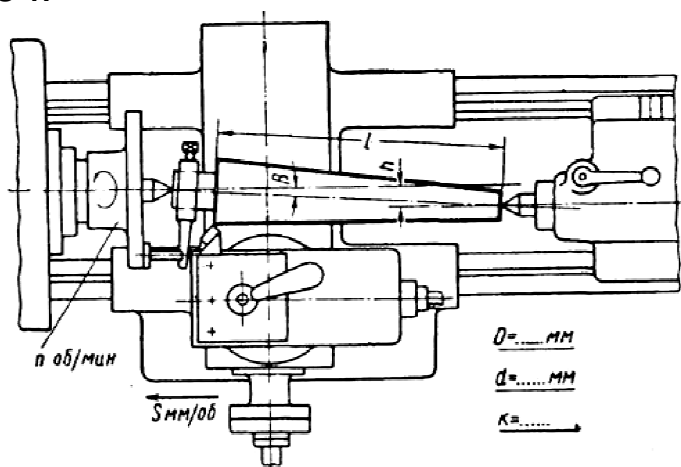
Схема наладки токарного станка на обработку конуса при сдвинутой задней бабке
